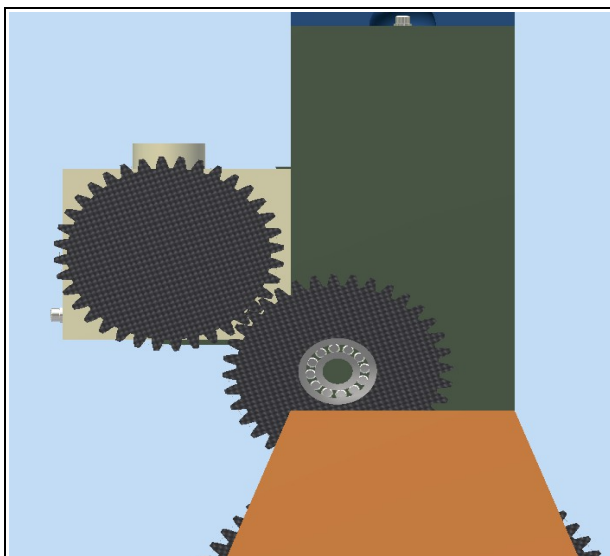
Engranaje eje de levas posicionado
